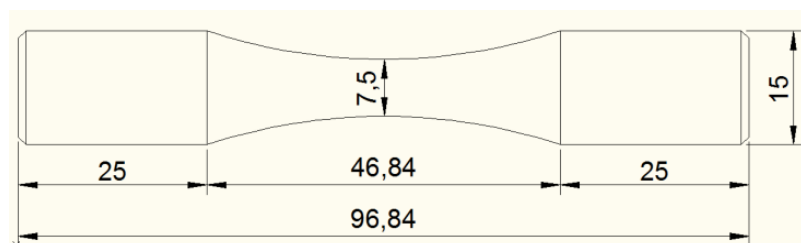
DIMENSIONES DE LA PROBETA ESTANDARIZADA
